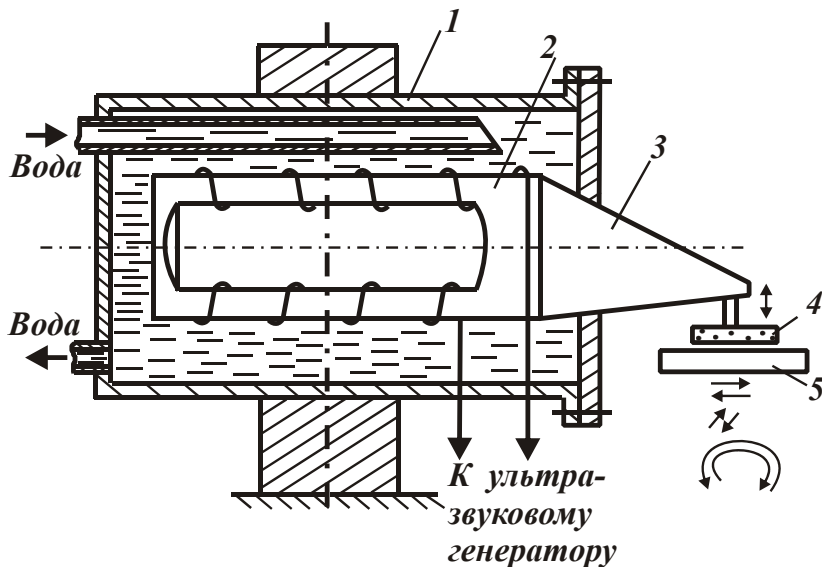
Схема плоского шлифования с применением ультразвука: 1 – корпус с водяным охлаждением; 2 – магнитоstrictionный преобразователь; 3 – концентратор; 4 – круг (брусок); 5 – деталь, изделие.
